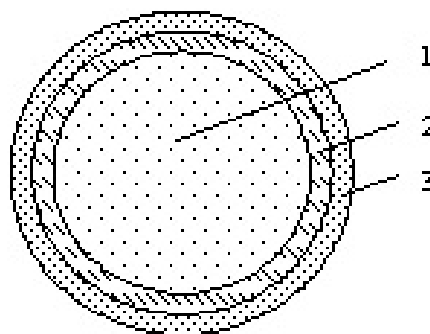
Расчетная схема конструкции: 1 – ТРТ; 2 – резина; 3 – материал типа "KEVLAR"
